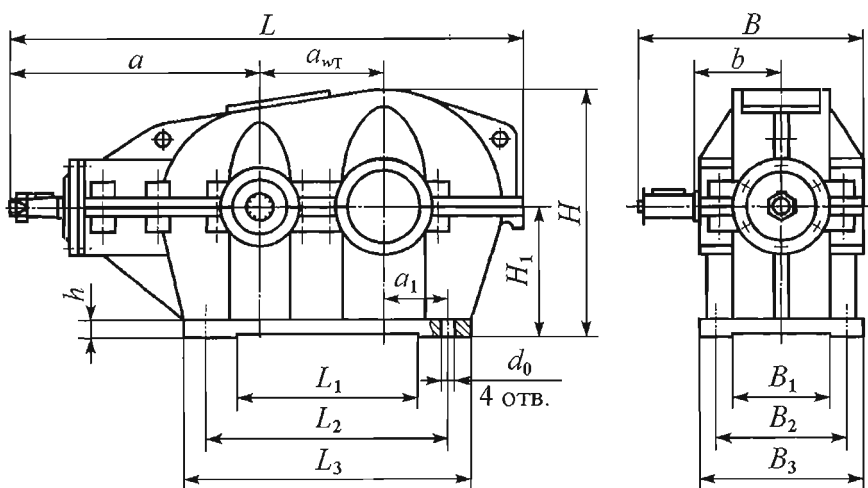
Габаритные, установочные и присоединительные размеры редуктора
